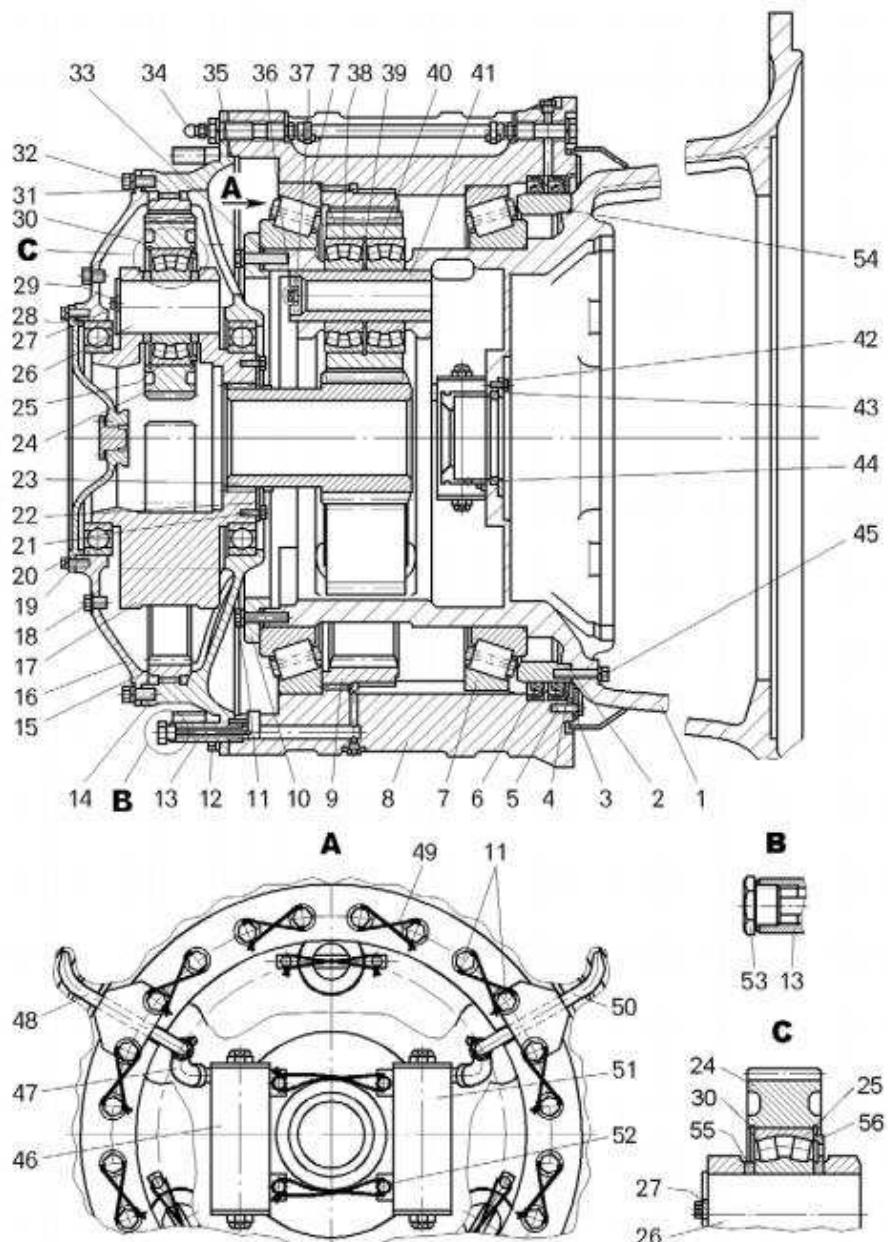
Редуктор электромотор-колеса: 1 – корпус редуктора; 2 – кольцо подманжетное; 3 – прижим; 4 – кольцо дистанционное; 5, 12, 21, 29, 32, 36, 42, 45, 52 – болты; 6 – манжета; 7, 19, 25, 38 – подшипники; 8 – ступица; 9 – коронная шестерня второго ряда; 10 – кольцо упорное; 11 – болт регулировочный; 13 – трубка сливная; 14 – крышка ведущая; 15 – коронная шестерня первого ряда; 16 – крышка водила первого ряда; 17 – водило первого ряда; 18 – пробка контрольная; 20 – крышка редуктора; 22, 27, 37 – пластины стопорные; 23 – солнечная шестерня второго ряда; 24 – сателлит первого ряда; 26 – ось сателлита первого ряда; 28, 31, 35, 54 – кольца уплотнительные; 30, 39 – кольца стопорные; 33 – распорное кольцо; 34 – масленка; 40 – сателлит второго ряда; 41 – ось сателлита второго ряда; 43 – кольцо; 44 – манжета; 46, 51 – фильтры; 47 – шланг соединительный; 48, 50 – маслоуловители; 49 – шплинт; 53 – щуп; 55 – кольцо распорное; 56 – пластина упорная
